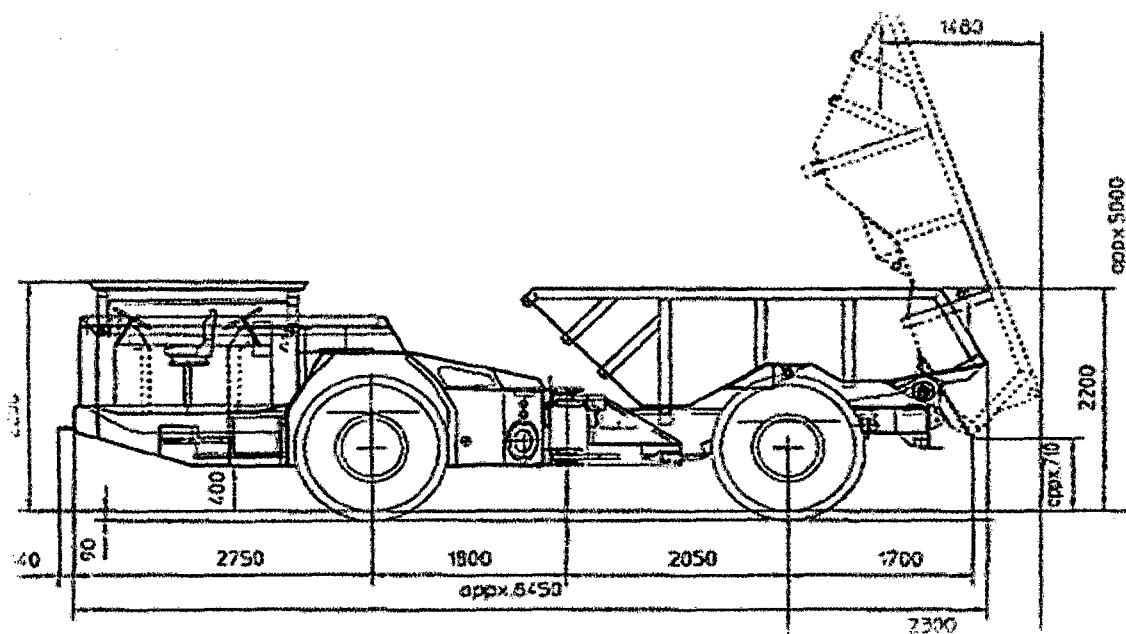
Muestra las dimensiones en la posición como se ve.
